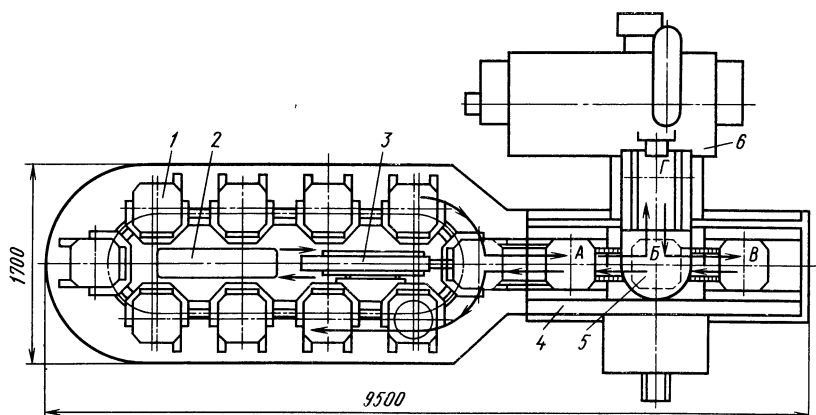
Транспортная система с индивидуальным конвейером-накопителем: А, Б, В, Г — позиции спутников на станке, 1 — приспособления-спутники с корпусными деталями и режущим инструментом; 2 — привод, 3, 4 — челночное устройство; 5 — стол станка; 6 — многоцелевой станок
